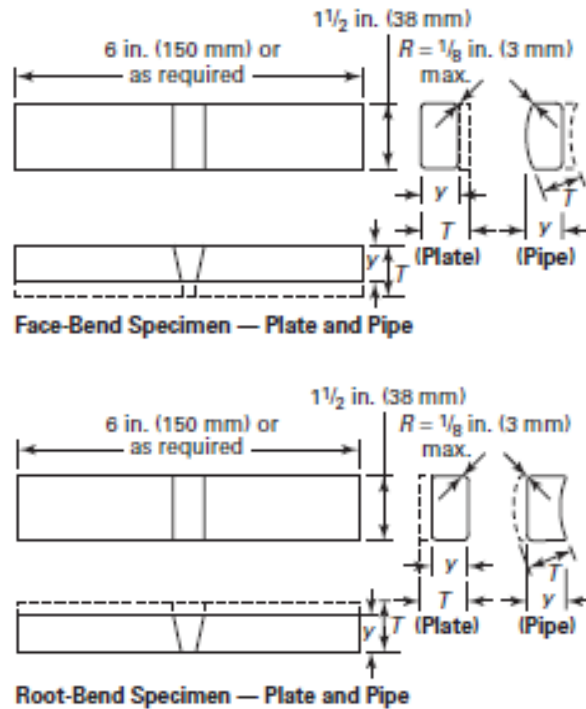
Probetas para ensayo de doblez guiado en uniones soldadas – Doblez de cara y de raíz (Tomado del código ASME Boiler and Pressure Vessel 2010 Adenda 2011. American Society of Mechanical Engineers. Pág. 163)
